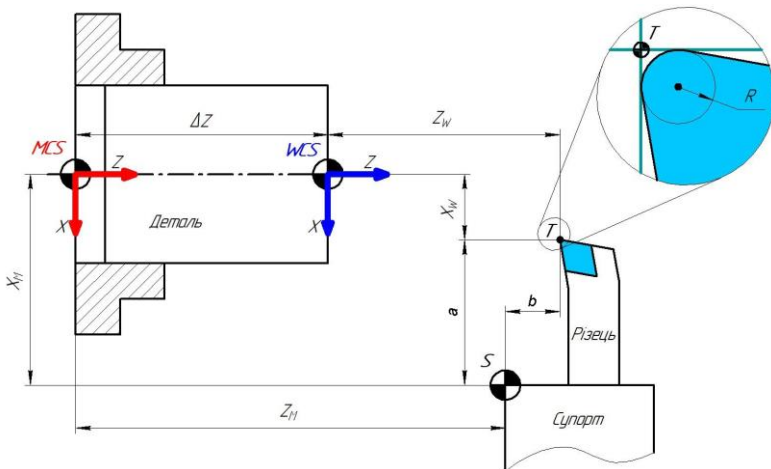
Схема систем координат токарного верстата з ЧПК
